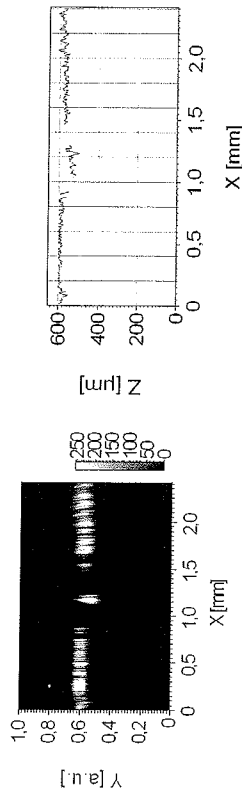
Messung einer Laserschweißnaht.
